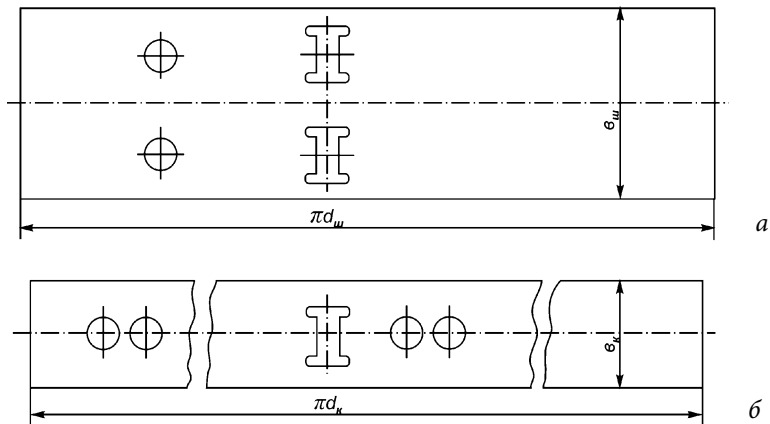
Ленты для восстановления шеек коленчатого вала двигателя : а – для шатунной; б – для коренной
